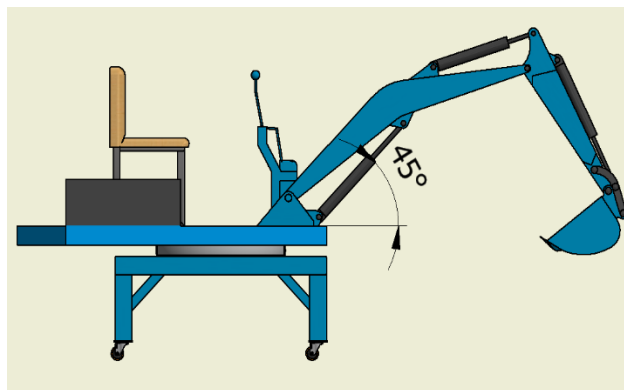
Penentuan Posisi Fixed Constraint Pada Diameter Boom Silinder 3D Excavator
